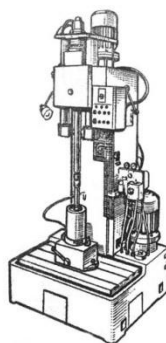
Общий вид хонинговального станка 3K833
